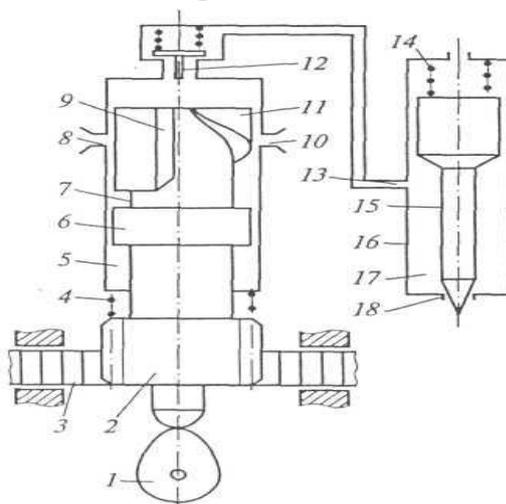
Схема работы топливного насоса высокого давления: 1 - эксцентрик; 2 - шестерня; 3 - рейка; 4, 14 - пружины; 5 - гильза; 6 - плунжер;
